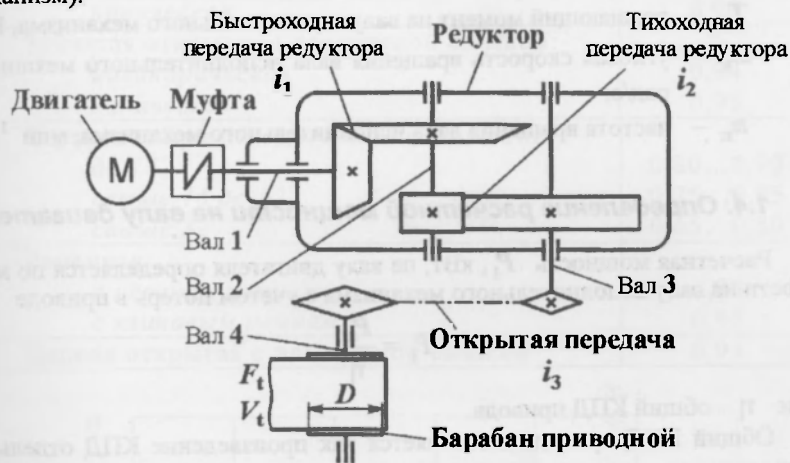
Кинематическая схема привода ленточного конвейера
